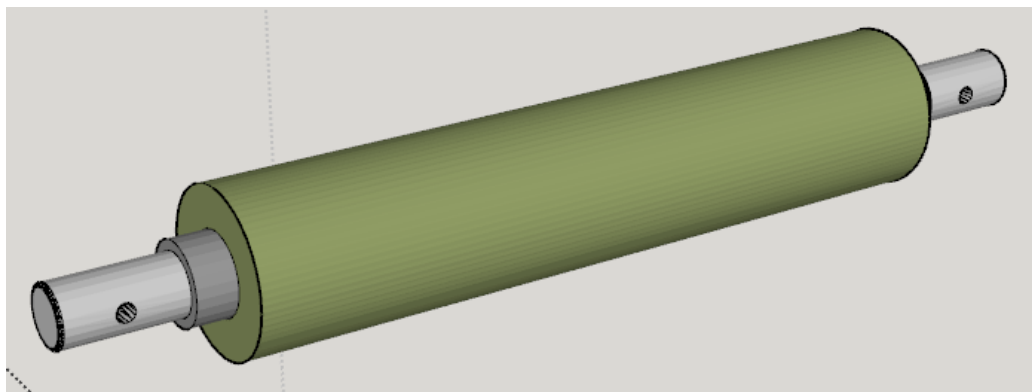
Вал для обертю конвеєрної стрічки
